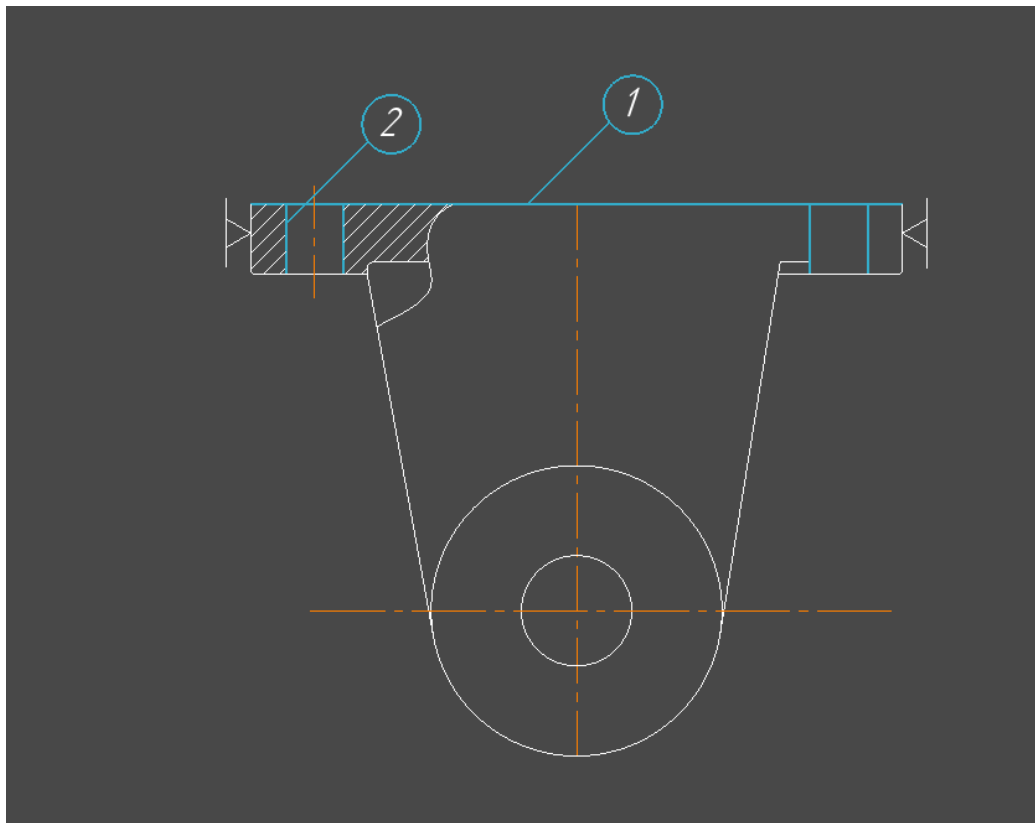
Перша операція фрезерування нижньої частини та свердління отворів
